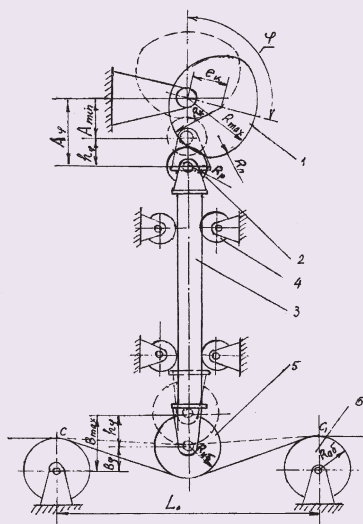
Схема кулачкового механизма: 1-кулачок; 2-ролик; 3- толкатель; 4-опорный ролик; 5-натяжной блок; 6- опорный блок
